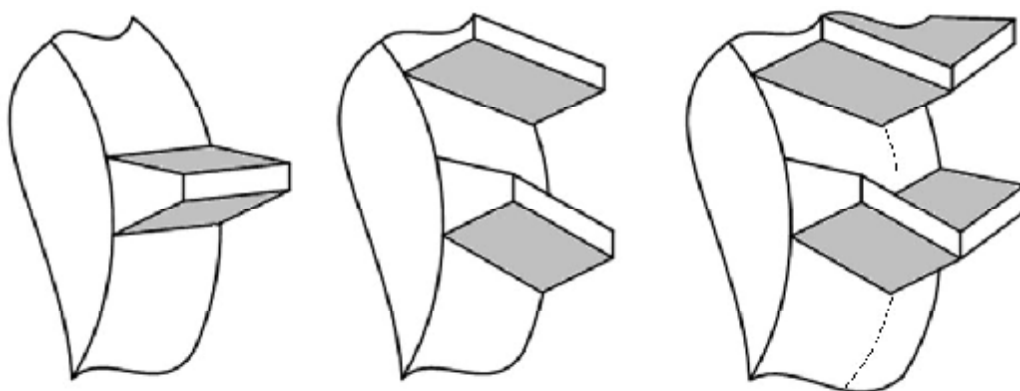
прямозубое, косозубое и шевронное зубчатое колесо
